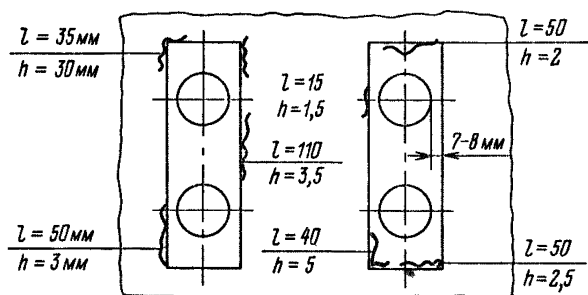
Расположение трещин в местах приварки деталей внутрибарабанных устройств.
